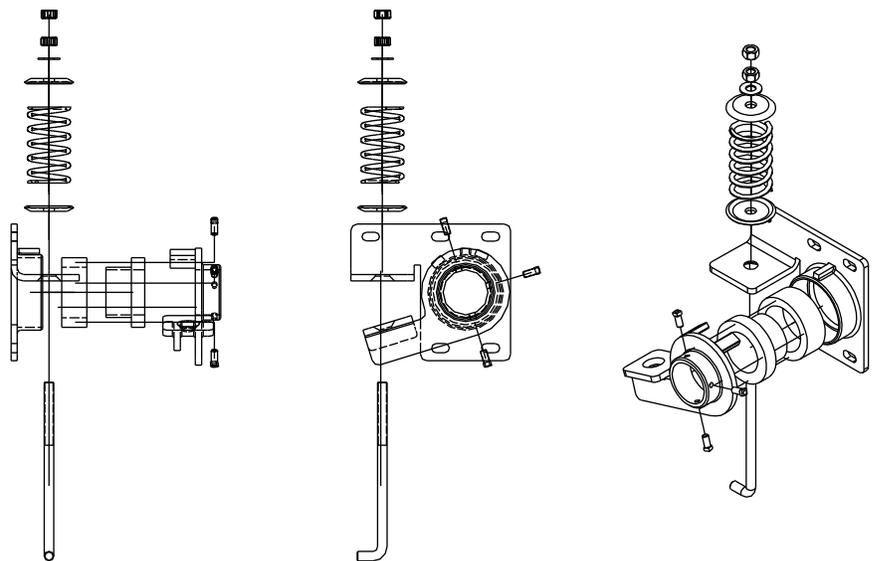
Ensablaje del Sistema Tensor Spring-Shoc
